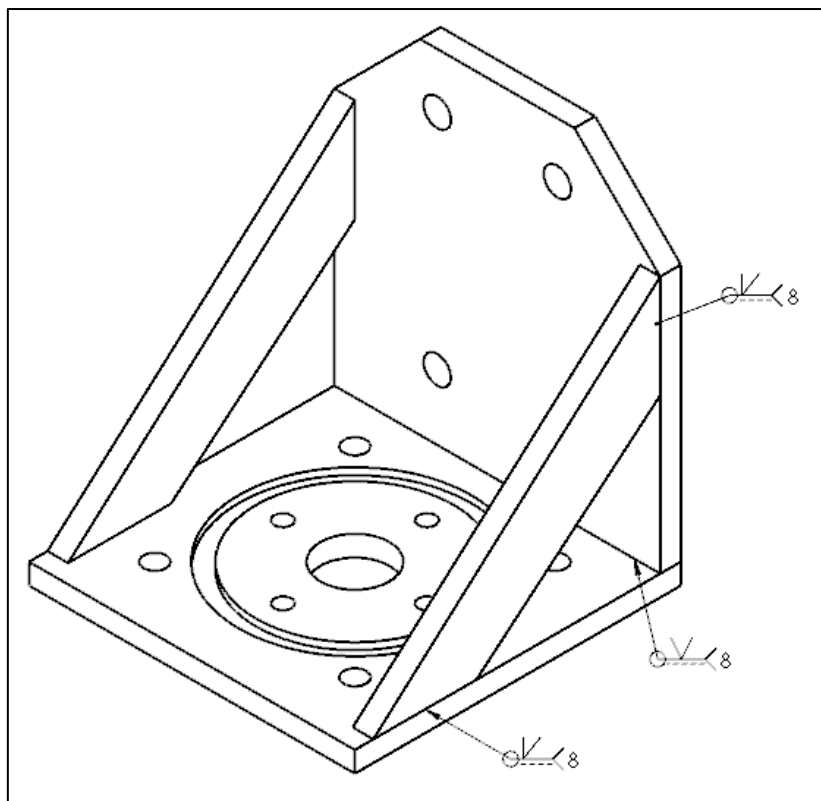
Vista isométrica do conjunto suporte do motor, com indicação dos cordões de solda
